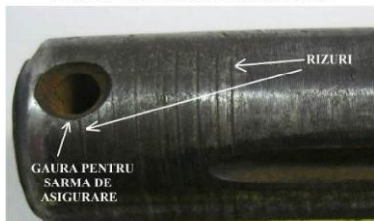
Detaliu riziuri pe suprafața de contact a bolțului cu falca inferioară a barei de tracțiune
